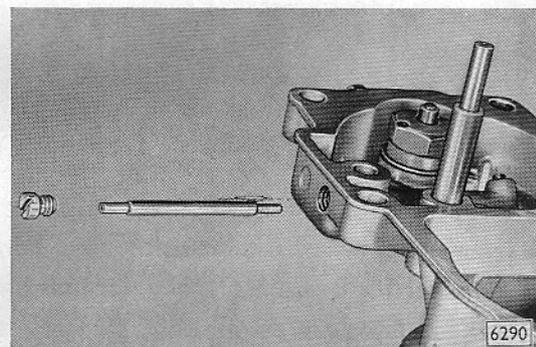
Zylinderschraube (Messing) und Füllstift aus Vergaserdeckel entfernt
